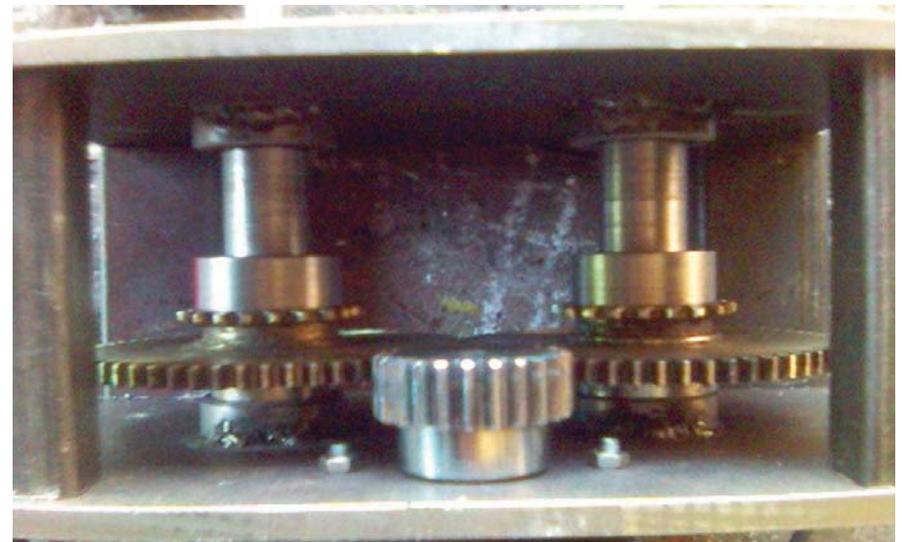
Sistema de transmisión montado. Engrane menor transmite el movimiento desde el motor, haciendo rotar los engranes mayores, que a su vez hacen rotar las masas de acero.
